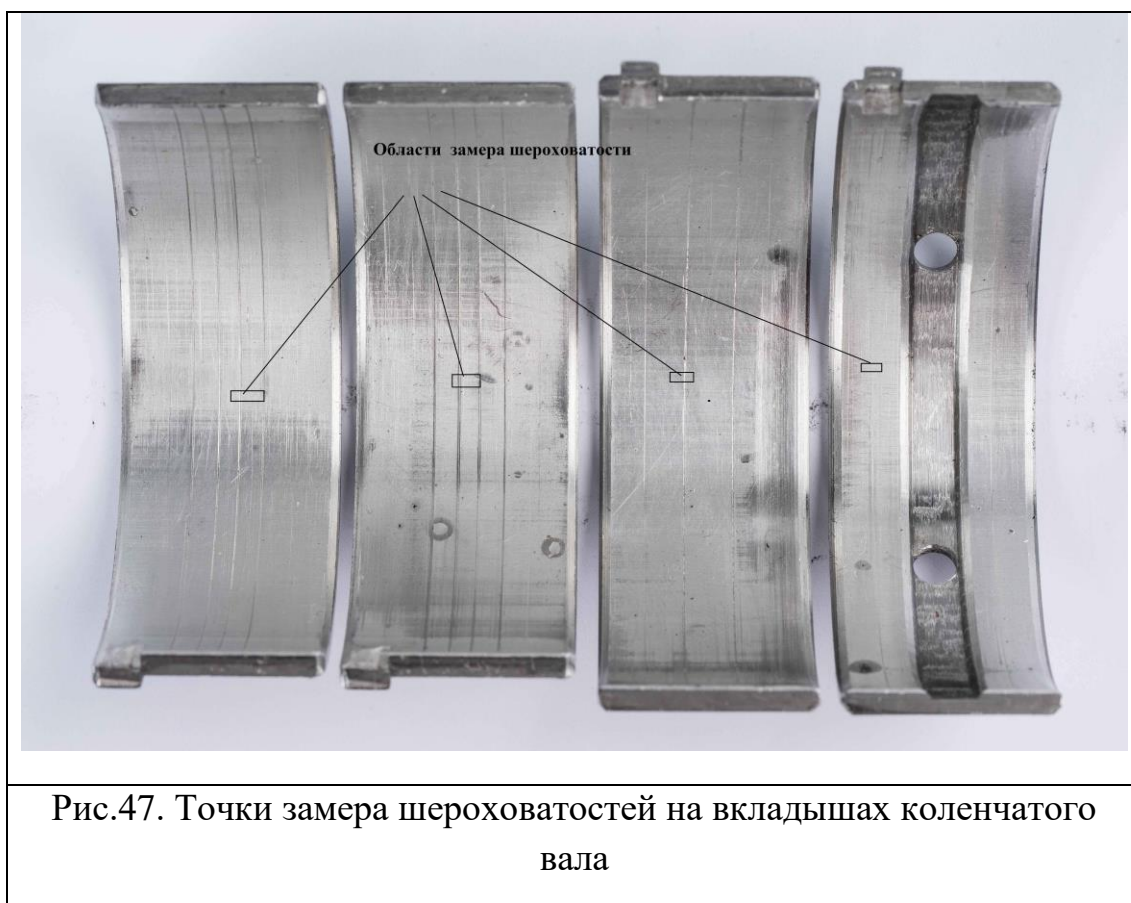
Точки замера шероховатостей на вкладышах коленчатого вала
